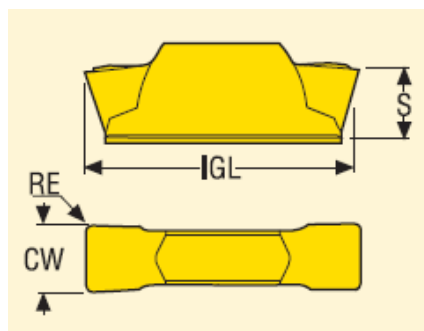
Форма пластины LCMF160608-0600-FT
